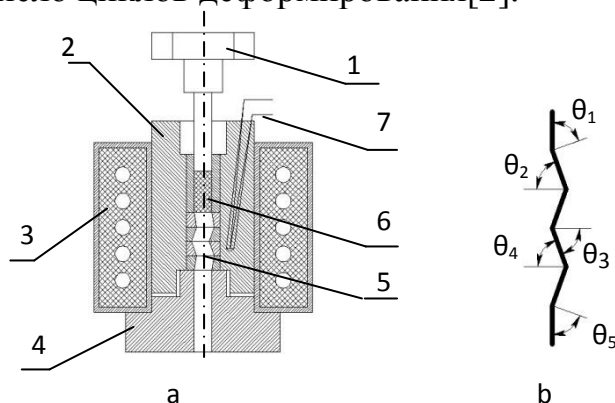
Схема экспериментальной ячейки (a) и угловых каналов (b) для реализации РКМУТФЭ: 1 - пуансон; 2 - ячейка; 3 - нагревательный элемент; 4 - основание; 5 - деформирующий блок; 6 - образец; 7-термопара.
